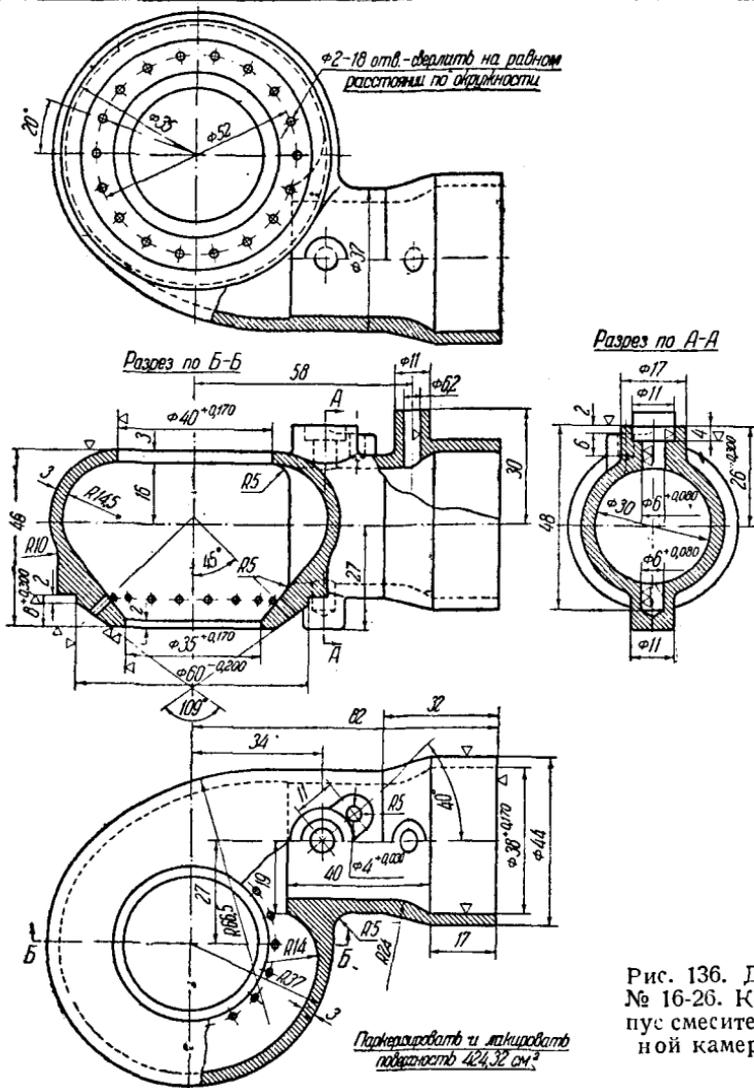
Дет. № 16-26. Корпус смесительной камеры
